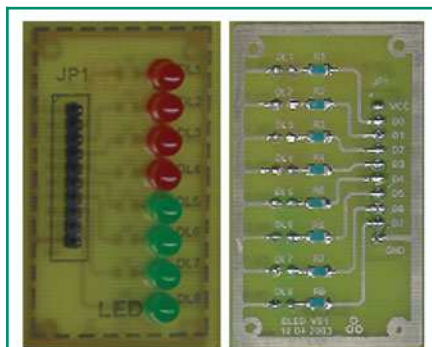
Prototipo del modulo led (lato saldature e lato componenti)
